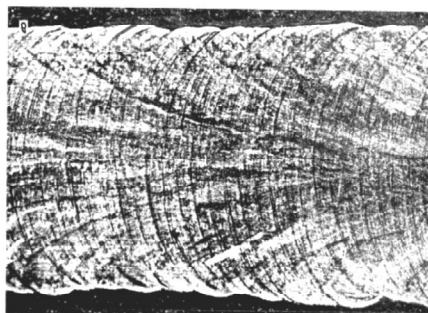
Внешний вид поверхности сварного шва с чешуйчатым строением, $\times 5$
